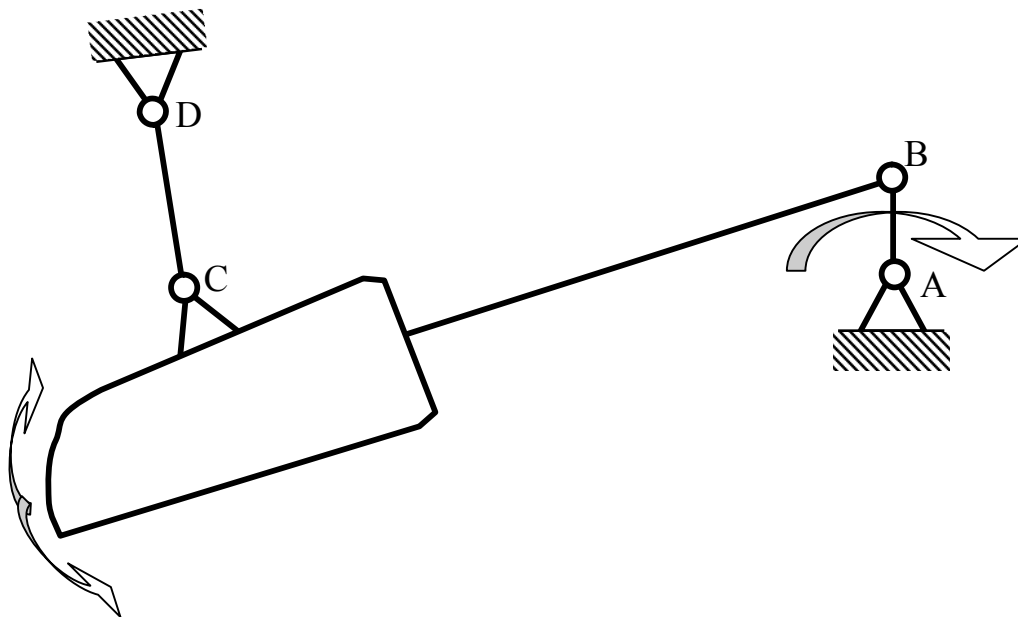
Схема механизма привода лемеха картофелеуборочного комбайна ККУ-2А «Дружба»
